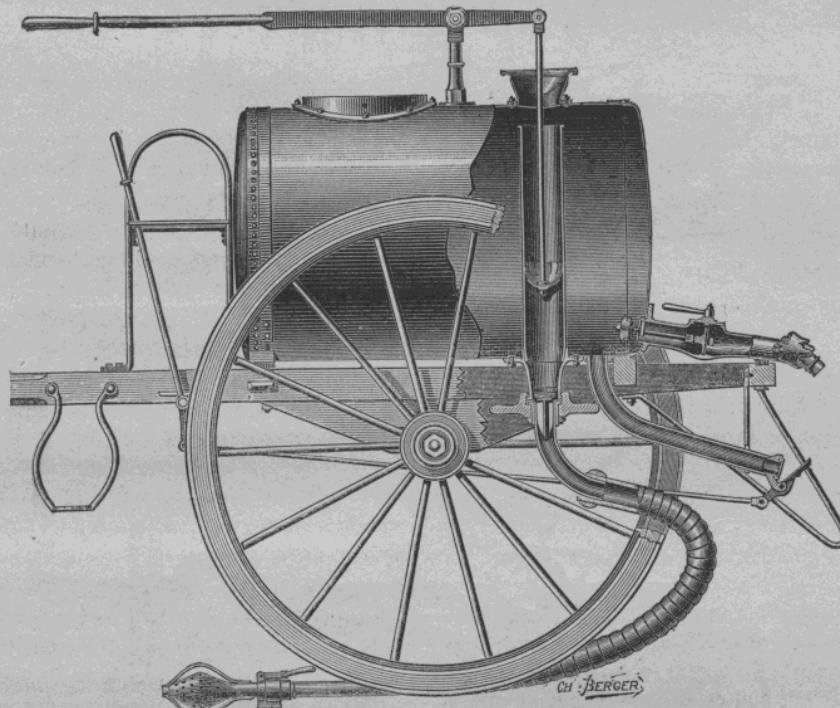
Coupe longitudinale d'un tonneau à purin.
